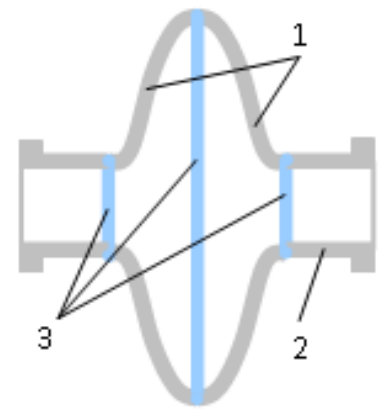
Сверхпроводящий резонатор: 1 – получашка, 2 – трубка дрейфа, 3 – сварной шов.
